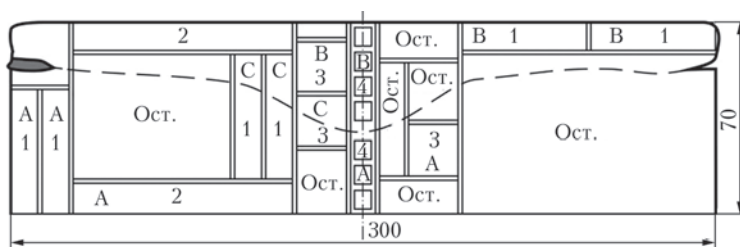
Схема вырезки образцов: зона А — основной металл; В — наплавленный металл; С — переходной слой
